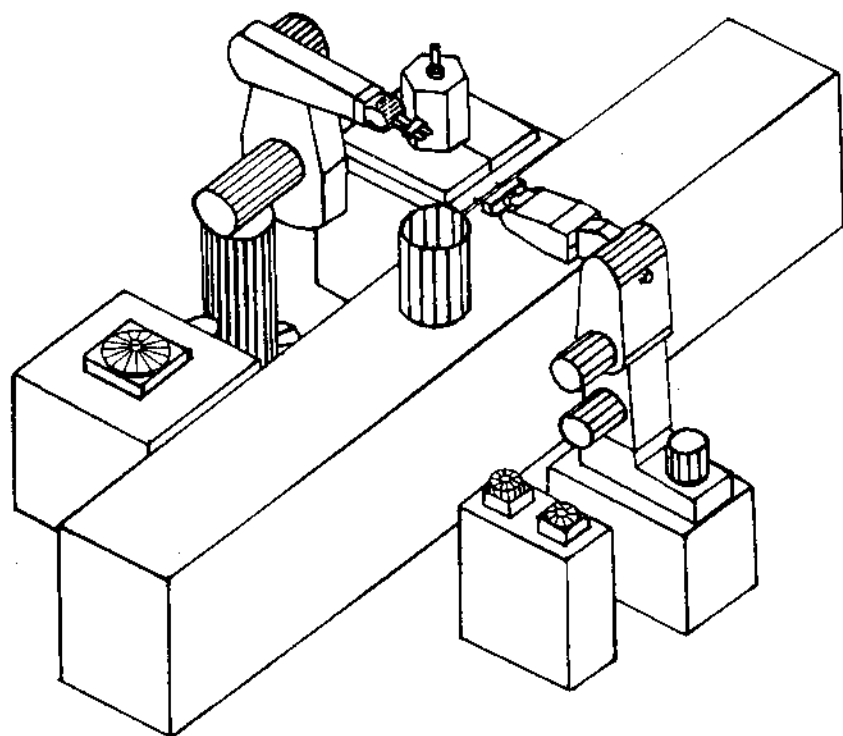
Tay máy SCARA ( Selective Compliance Assembly Robot Arm )
